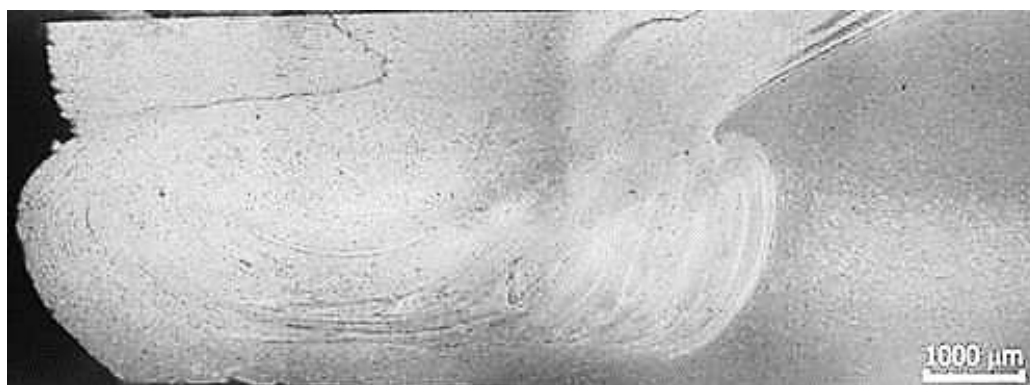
Разрушение сварного шва сплава 1565ЧМ с дефектом в виде линии стыка при испытании на растяжение
